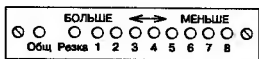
Общий вид платы для выводов первичной обмотки сварочного аппарата
